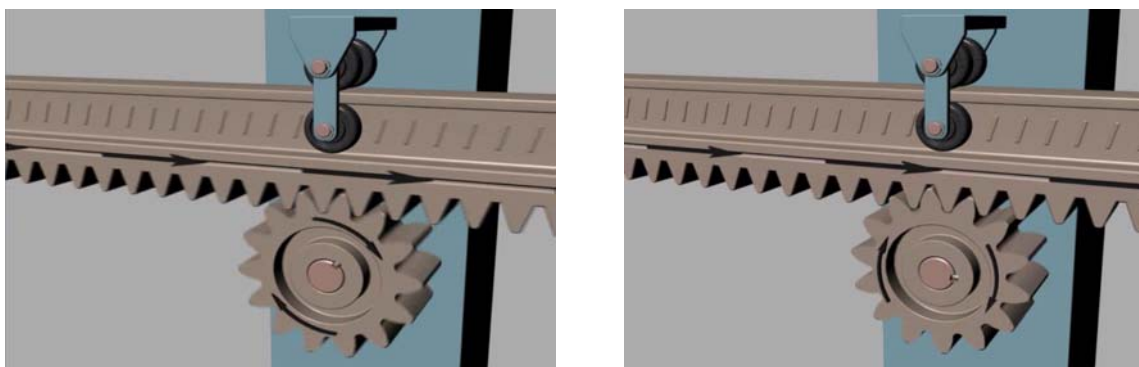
3D модель рейкової передачі (рейка рухома)
